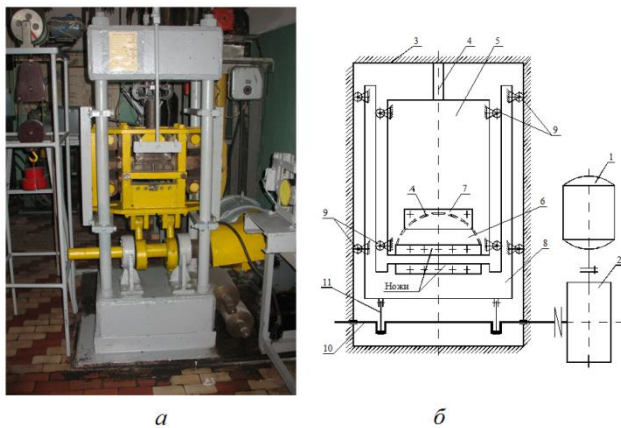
Общий вид кривошипно-шатунных лабораторных ножниц: а- с параллельным расположением суппортов; б - их конструктивная схема лабораторных ножниц
